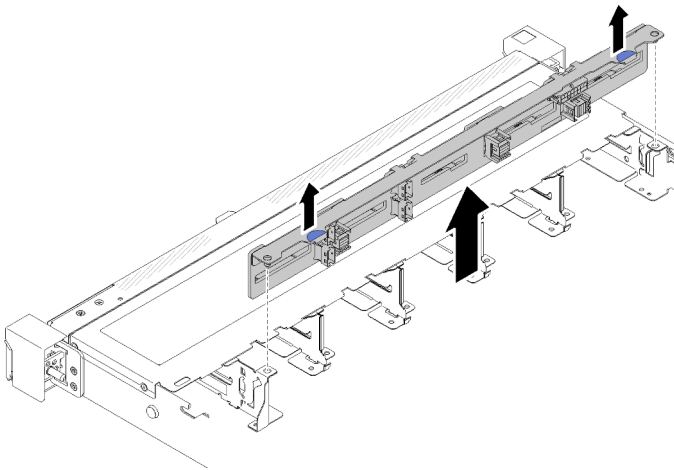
Retrait du fond de panier d'unité remplaçable à chaud 2,5 pouces
